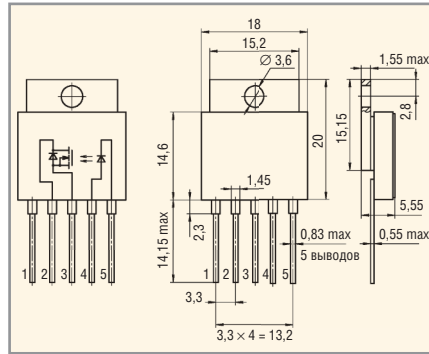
Чертёж корпуса и электрическая схема реле 5П163
